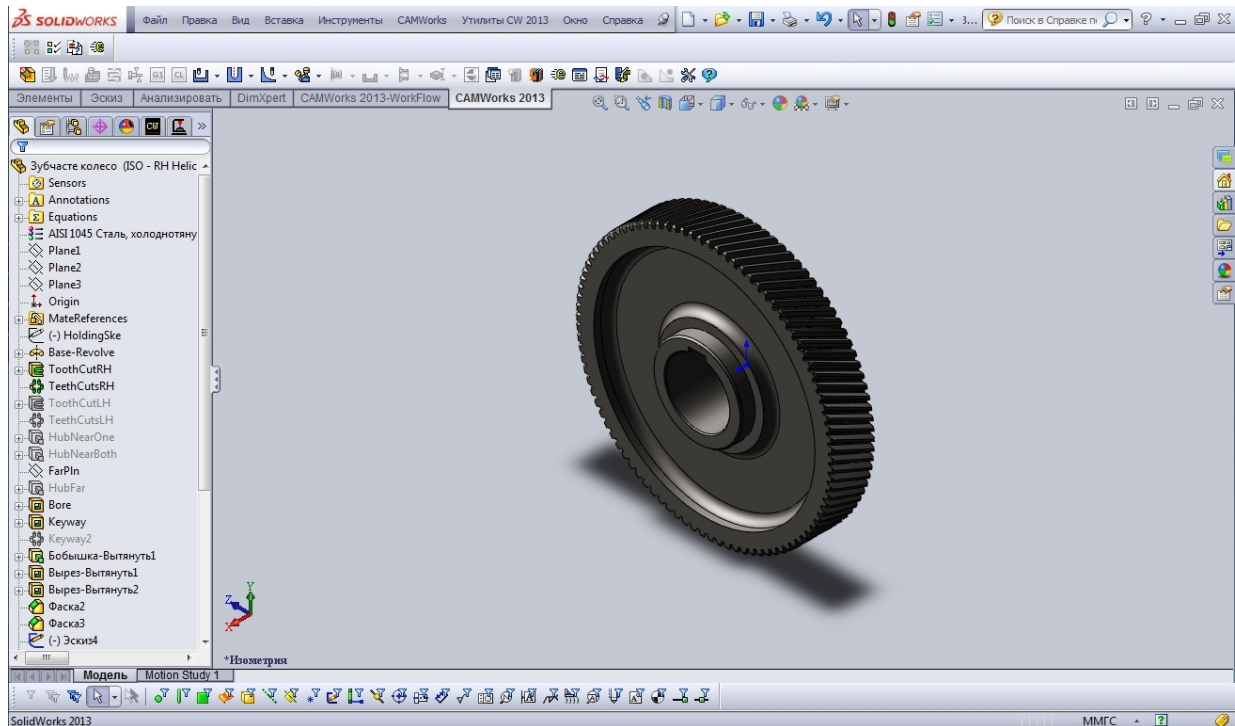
Модель деталі «Колесо зубчасте 254-13.00.000» з деревом побудови
